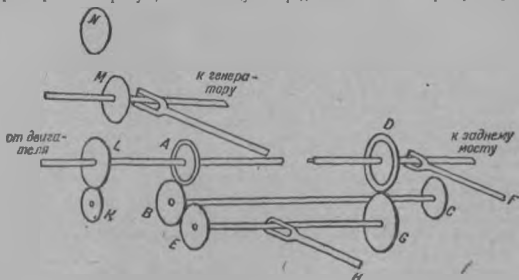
Кинематическая схема редуктора ПО-15-8.
